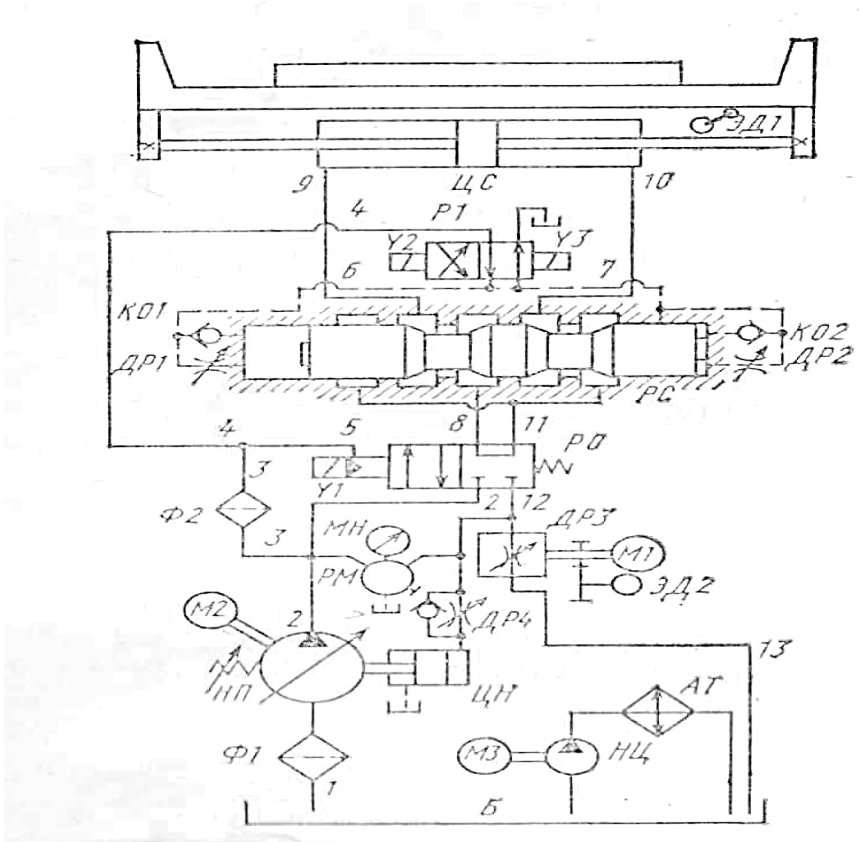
Гидравлическая схема плоскошлифовального станка 3Л1722В.
